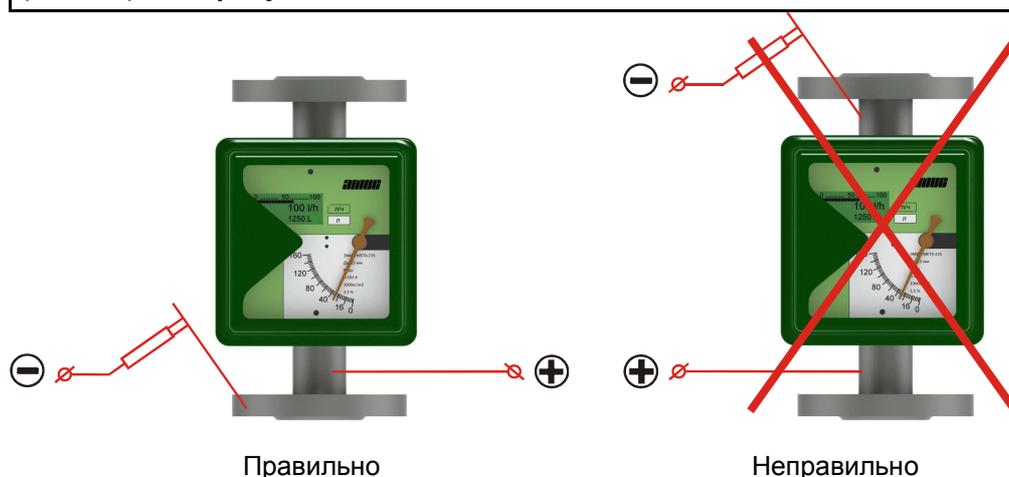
Подключение источника тока при электродуговой сварке с использованием ротаметра
